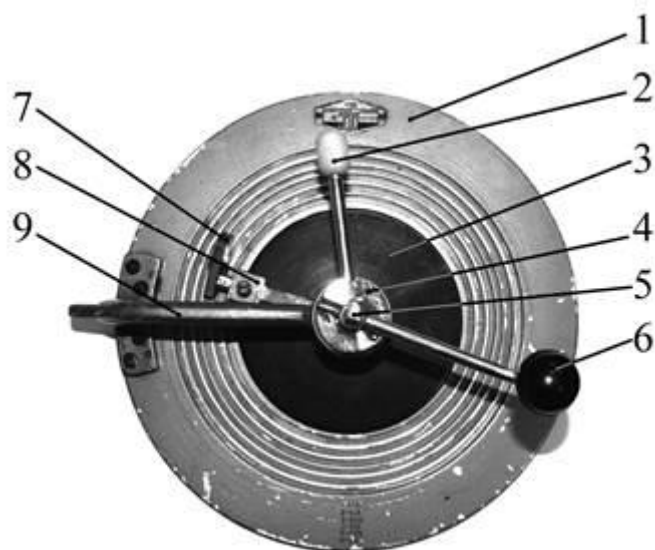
Приспособление ТММ-31А для изготовления бумажных заготовок
